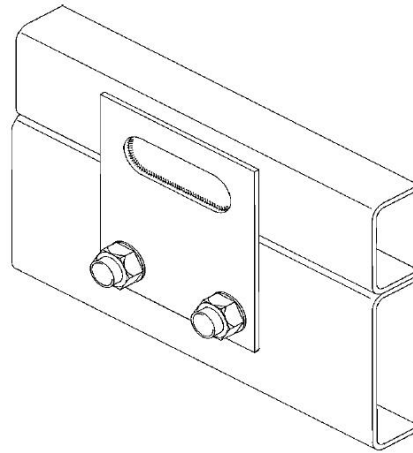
Hilfsrahmenbefestigung mit Lochschweißung ESC-025
